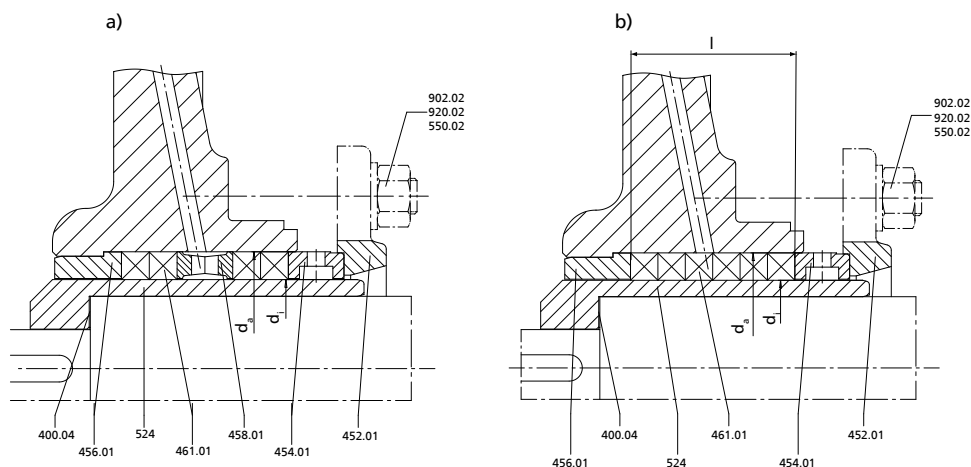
Монтаж набивочной камеры сальника а) с блокировочным кольцом и б) без блокировочного кольца
